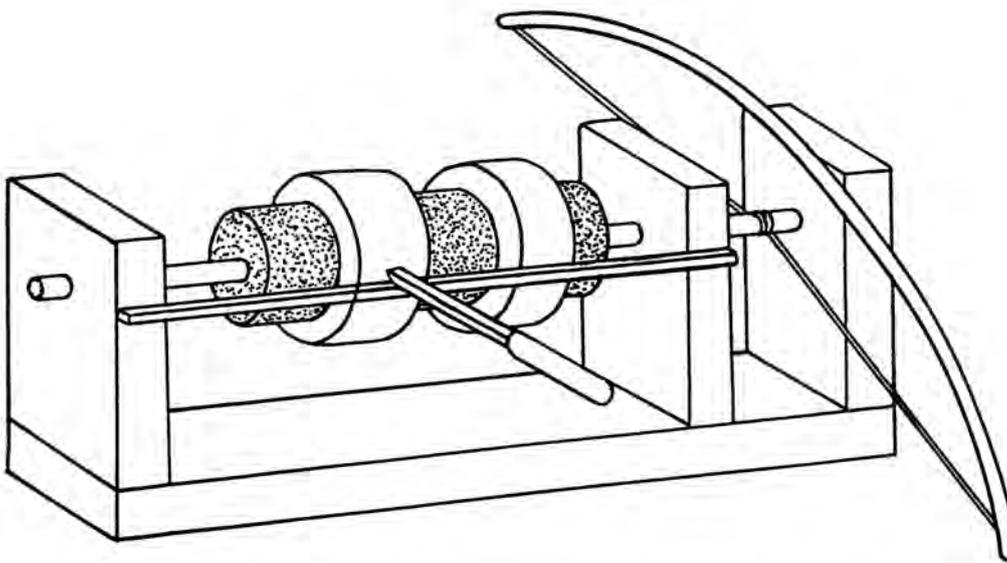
Reconstruction d'un tour à archet avec support pour l'outil coupant.
